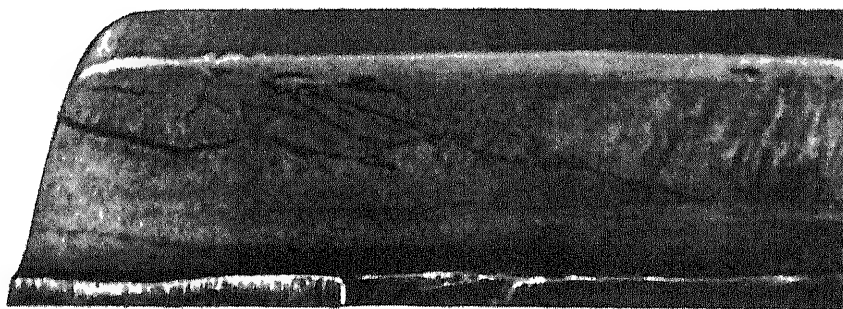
Трещины на боковой поверхности зуба передачи Новикова (по данным И.Н. Френкеля)
